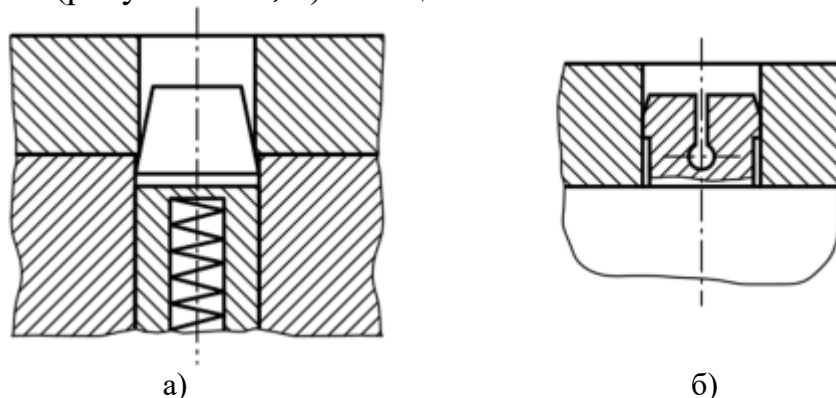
Схемы установки заготовки отверстием на подпружиненный конический (а) и упруго-деформируемый (б) пальцы
